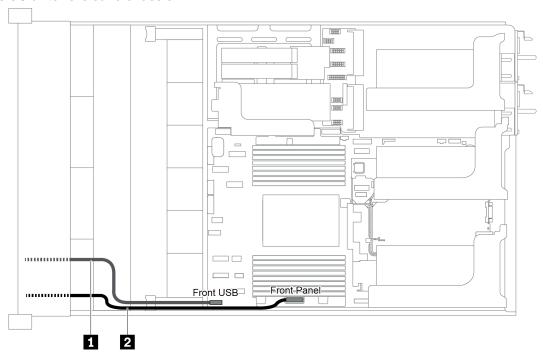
Instradamento dei cavi per l'assieme I/O anteriore sullo chassis
